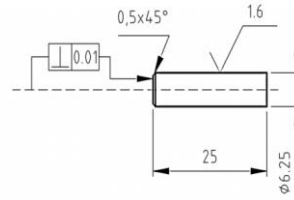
Dimensiunile pinilor din fontă [24], [66], [71]
